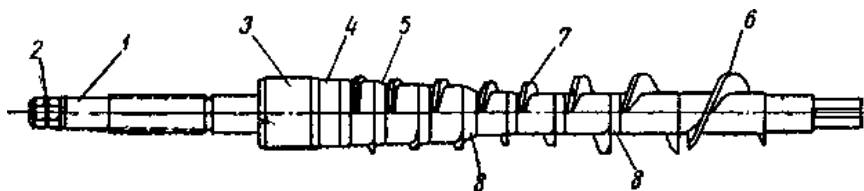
Ступінчастий вал форпреса ФП: 1 – сталевая вісь; 2 – затяжна гайка; 3,4 – циліндрові втулки; 5 – конічне кільце; 6 – подавальний виток; 7 – витки тиску; 8 – проміжні кільця
